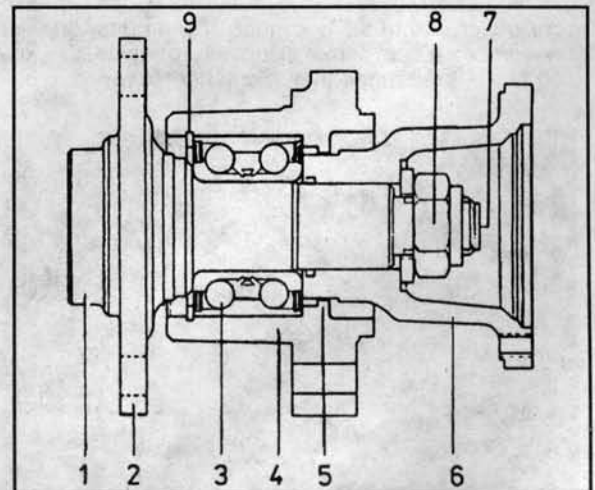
Новый вариант посадки подшипника колес задней оси
